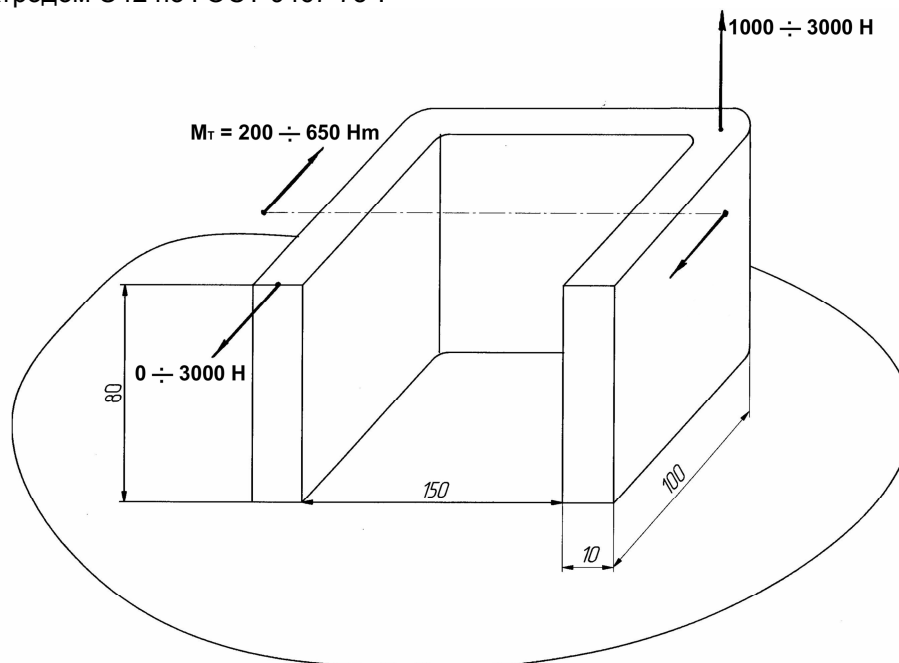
Расчетная модель таврового сварного соединения
